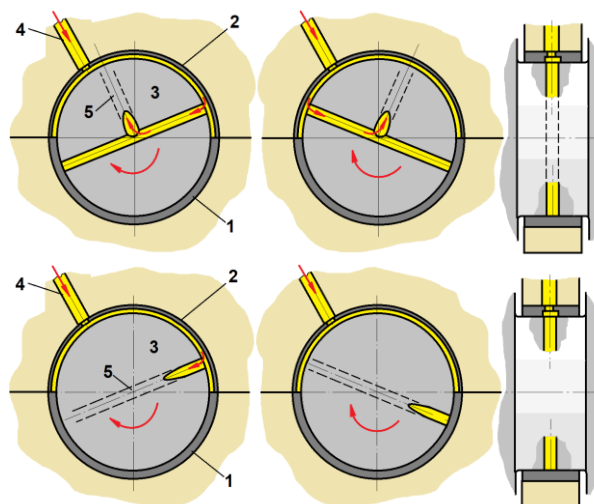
Конструктивные схемы коренного подшипника с непрерывной подачей масла через сквозное поперечное отверстие в коренной шейке (вверху) и с прерывистой подачей масла через отверстие, соединяющее коренную и шатунную шейки (внизу):
